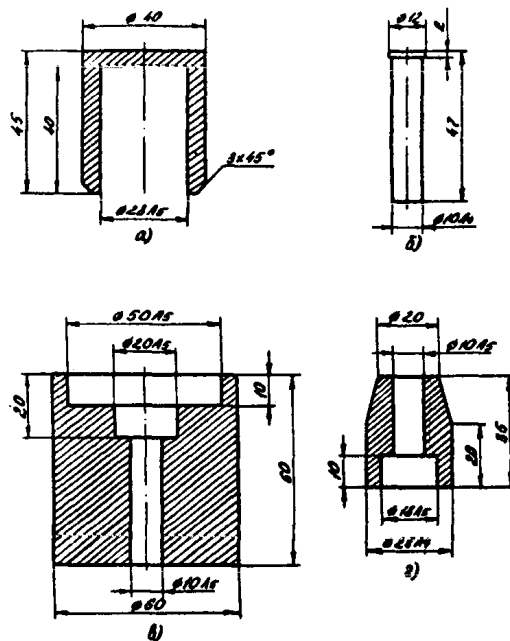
Приспособления для запрессовки резины в клапан блока включения или отключения (материал Ст 3):
